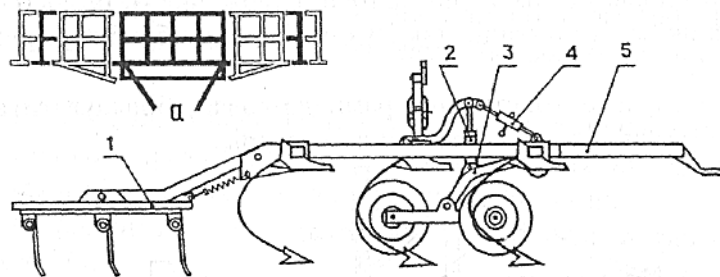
Культиватор фірми Degelman: а) схема секційної будови рами з доповненням бічних секцій; 1 - зубова борона; 2— гідроциліндр; 3 - балансирний механізм тандемних опорних коліс; 4 - гвинтовий обмежувач глибини ходу; 5 - телескопічне дишло причепа
